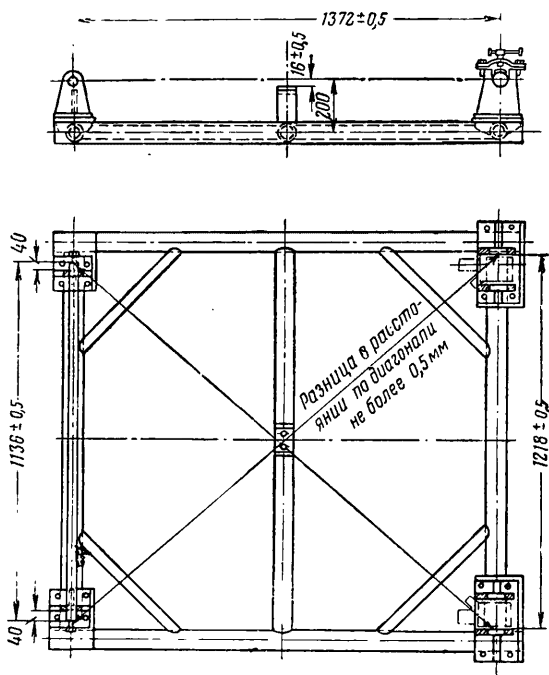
Кондуктор для проверки и сборки нижней рамы пантографа типа ДЖ-4
